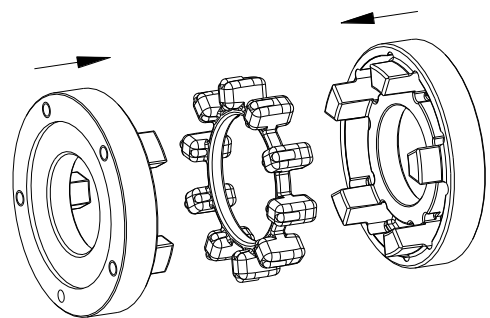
Montage der Mitnehmerflansche mit Elastomerring
